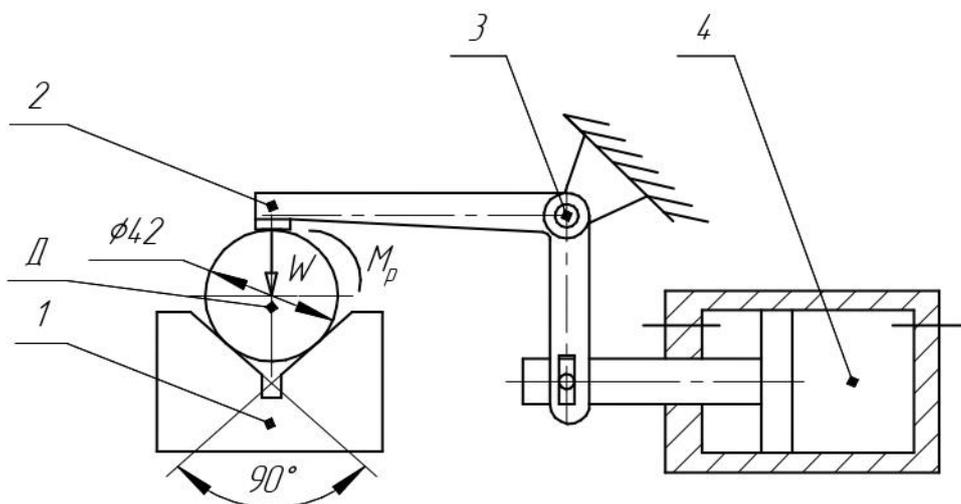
Кинематическая схема гидравлического зажима: 1 – Призма; 2 – рычаг; 3 – ось; 4 – гидроцилиндр; Д – деталь
